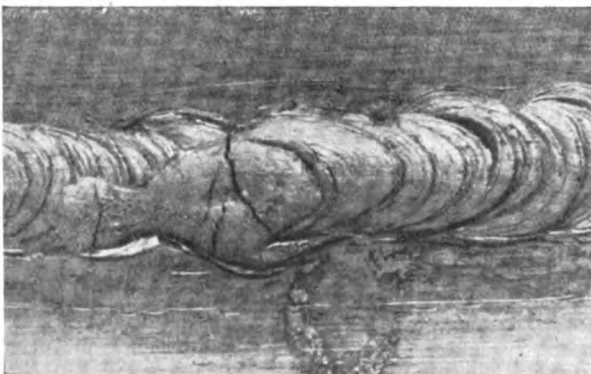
Risse in der Schweißnaht bei einem Pantalträger.
